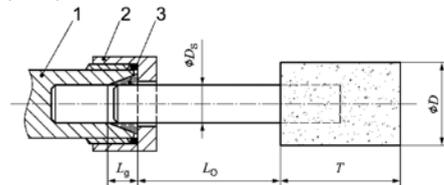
Lunghezza di bloccaggio del mandrino di serraggio e della pinza portautensili
